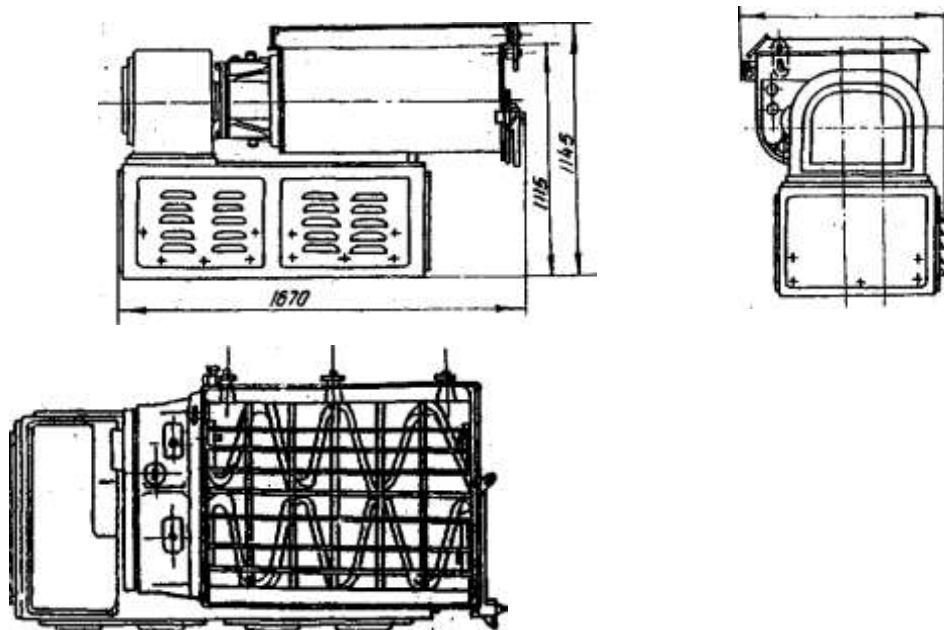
Общий вид фаршемешалки Л5-ФМБ
